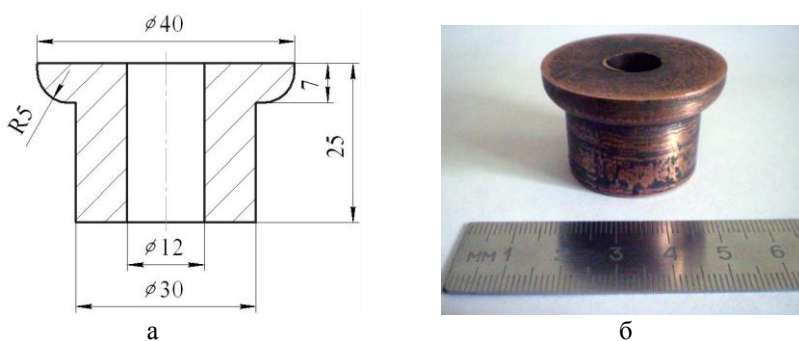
Заготовка деталі «втулка з буртом» після штампування:
